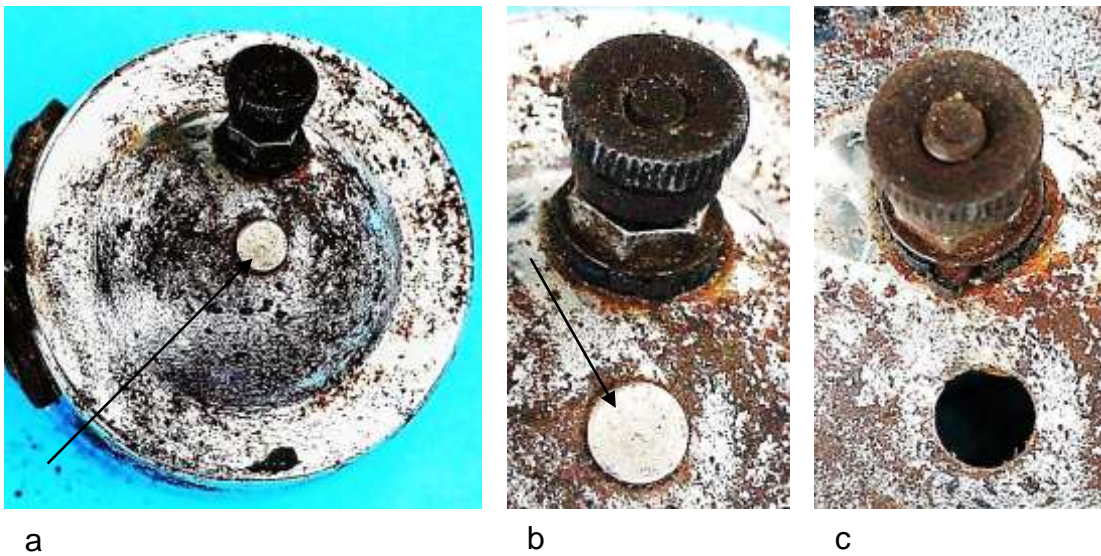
Bodenarmaturen; a) Bodenansicht mit Spurlager, b) Kabelanschluss und Lagerabschluss, c) Bohrung für den Passsitz des Lagers
